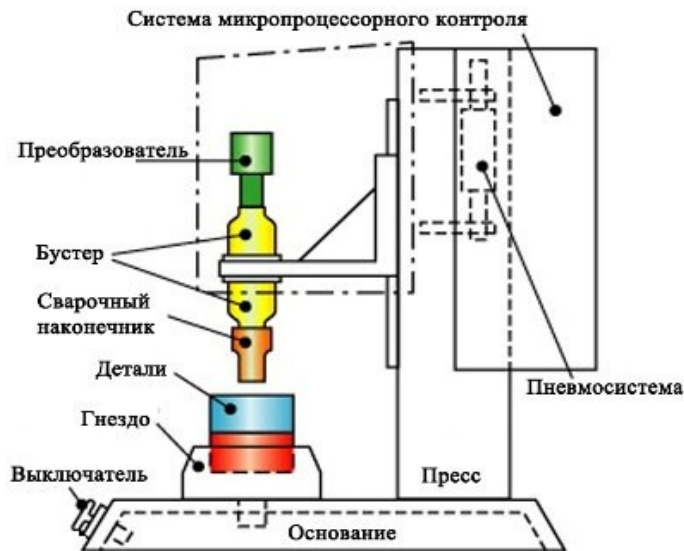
Схема установки для ультразвукового зварювання.
